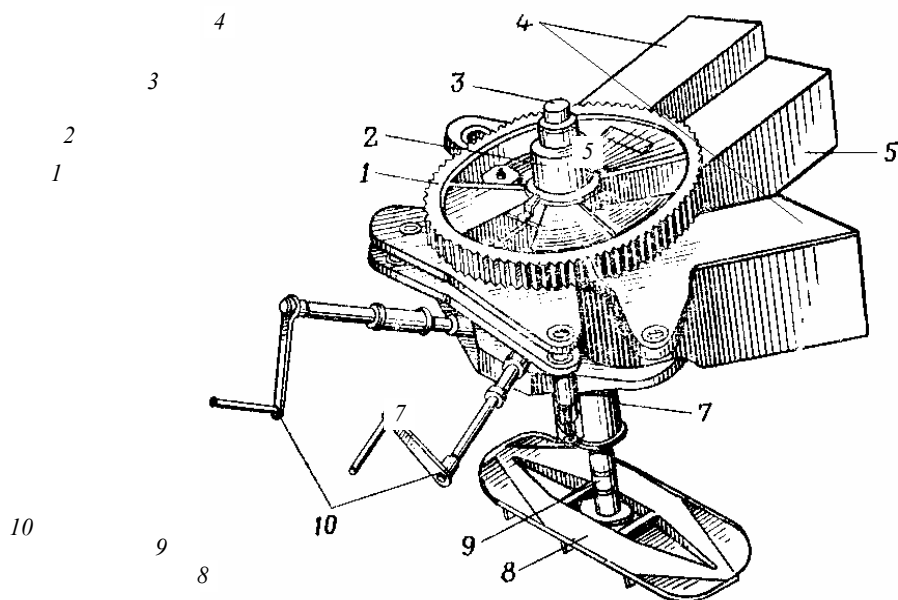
Нижний станок 122 мм гаубицы Д-30
